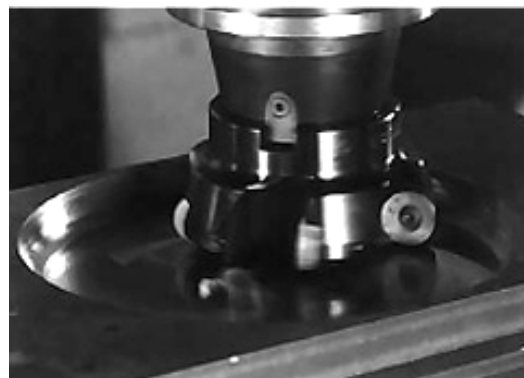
Торцеві фрези конструкції фірми *Sumitomo Electric
